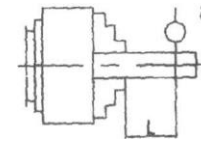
Токарный патрон с креплением за внешнюю поверхность заготовки с прямыми кулачками
